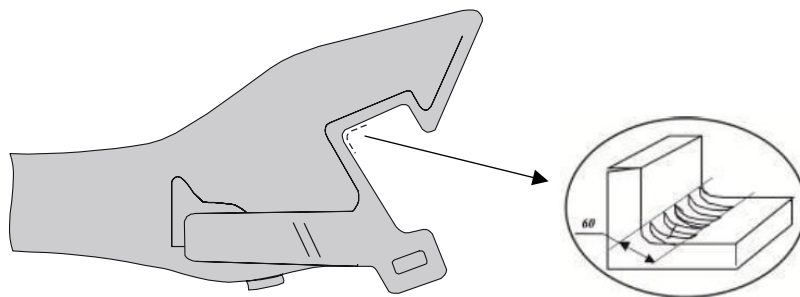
Схема сканирования угла сопряжения ударной и боковой поверхностей большого зуба
